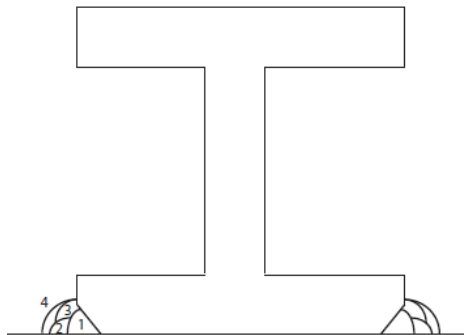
Soldadura entre la viga HEB160 y la estructura de la línea de pavonado. Elaboración propia.
